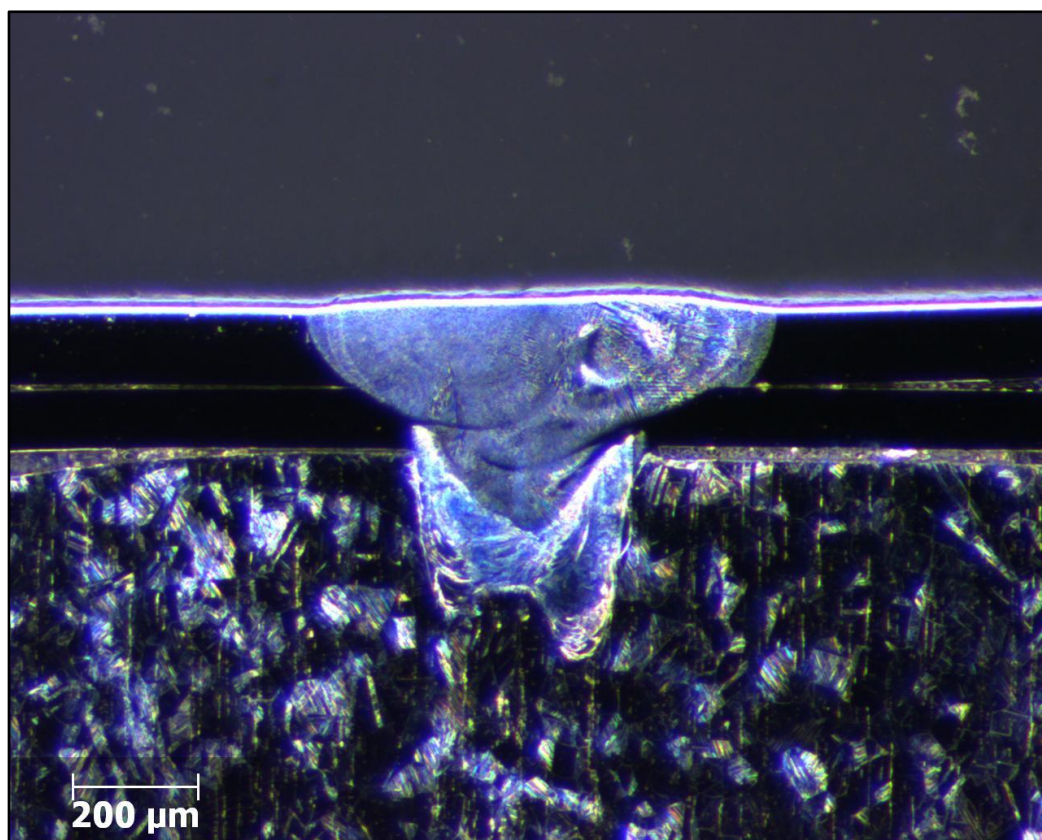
Die Schweißnaht wie in Abb. 8 unter dem Stereomikroskop – 100 x
